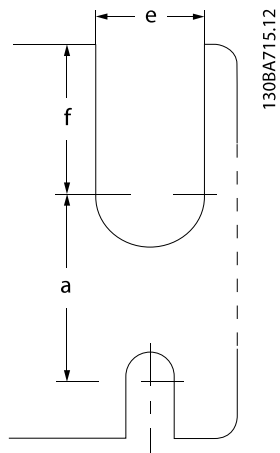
Pravilna montaža z zadnjo ploščo
